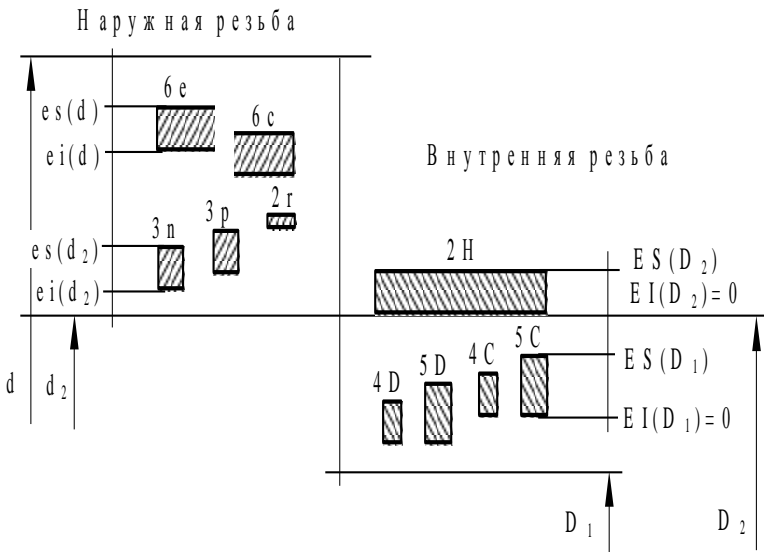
Расположение полей допусков резьбы с натягом
